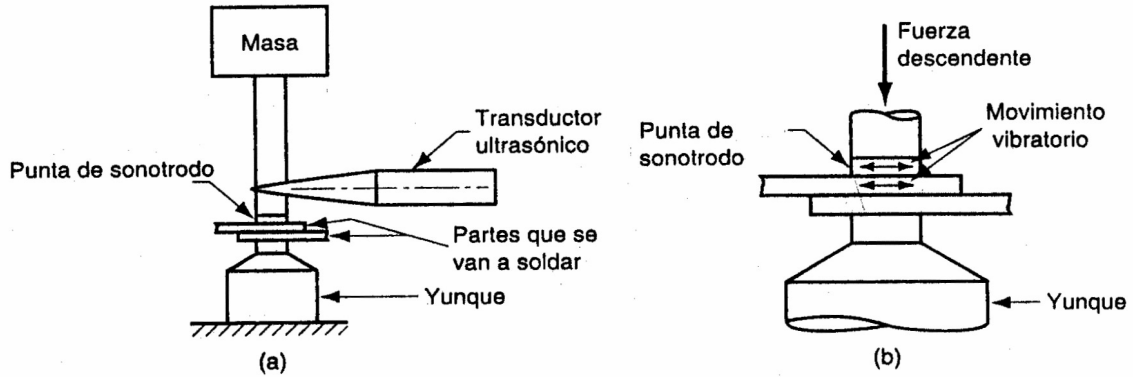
Soldadura ultrasónica (USW): (a) disposición general para una unión sobrepuesta y (b) acercamiento del área soldada.
